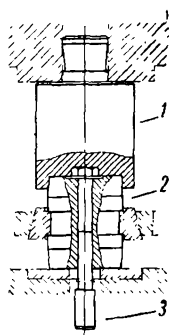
Типовой штамп для изготовления болта: 1 — верхняя часть штампа; 2 — нижняя часть штампа; 3 — выталкиватель
